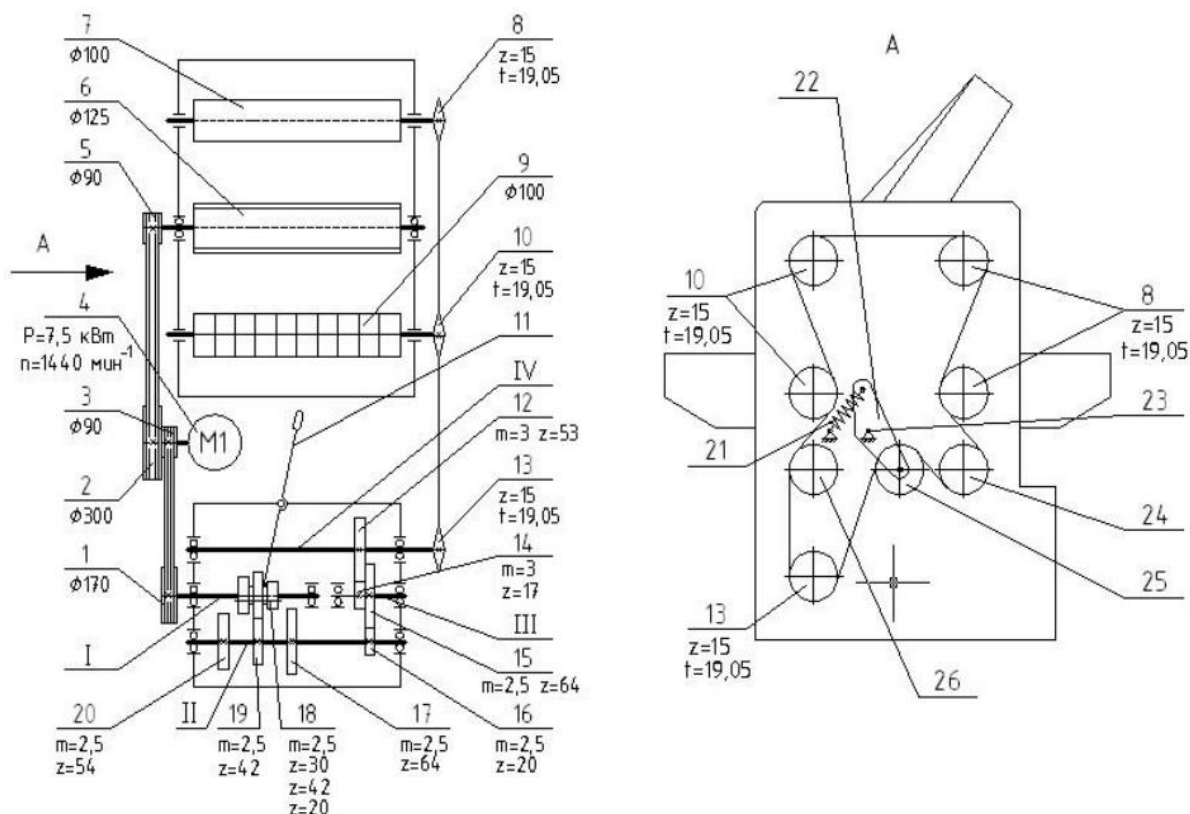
Рейсмусовый станок SUPERMAC 163
